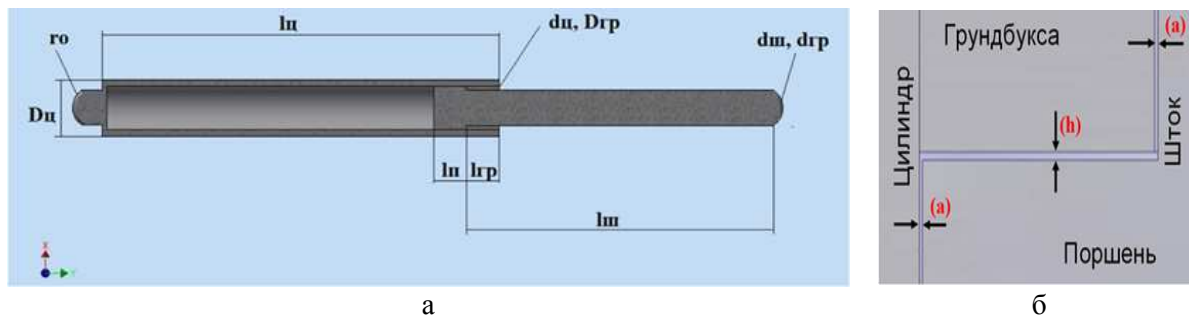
Принятые обозначения геометрических параметров деталей гидроцилиндра (а) и зазоров (б): D_u, d_u, L_u – наружный и внутренний диаметры, длина цилиндра, мм; r_o – радиус сферической опоры, мм; d_n, l_n – диаметр и длина поршня, мм; d_u, l_u – рабочий диаметр и длина штока, мм; D_{gp}, d_{gp}, l_{gp} – наружный и внутренний диаметры, длина грундбуксы, мм; a – зазоры между цилиндром и поршнем, грундбуксой и штоком, мкм; h – осевой зазор между грунддуксой и поршнем
